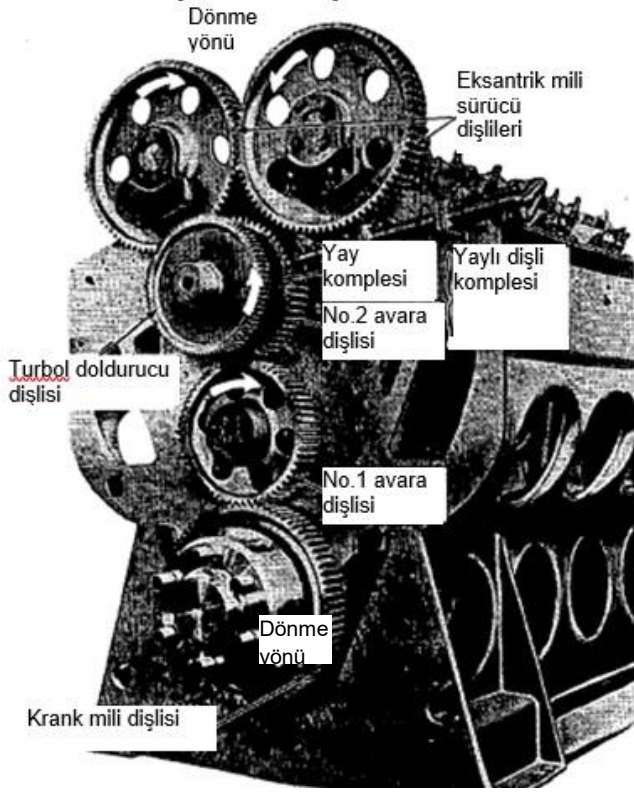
DE 33.000 Lokomotif Krank Mili Komitesi
